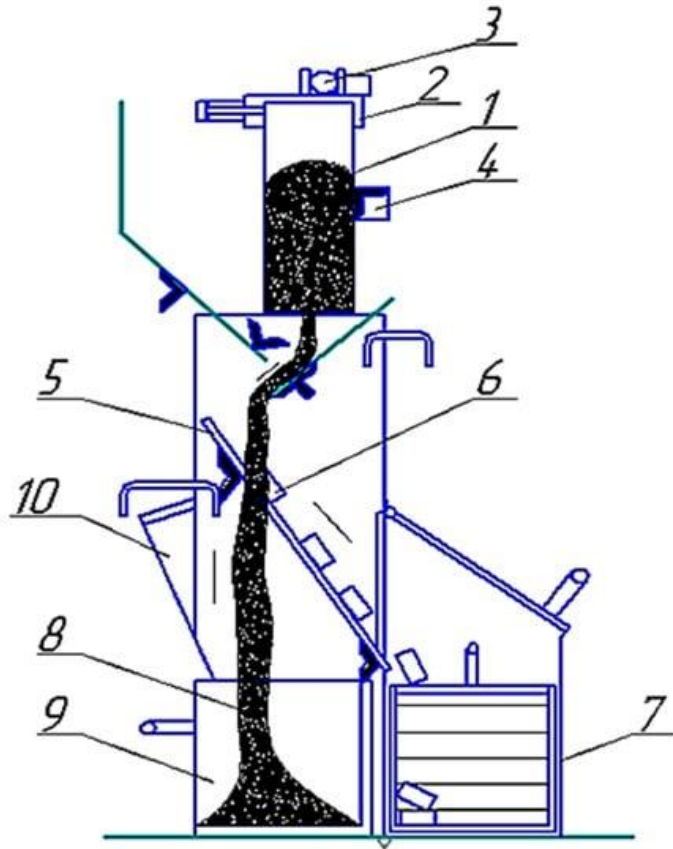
1.3 - Конструктивна схема сепаратора: 1—ємність; 2—розетка; 3—вал; 4—обмежувач; 5—похила решітка; 6—частини; 7—гартівний бак; 8—карбюризатор; 9—металевий контейнер; 10—кришка
